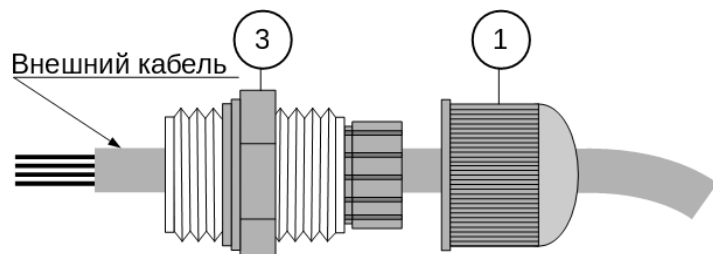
Установка ответной части корпуса разъема на внешний кабель
